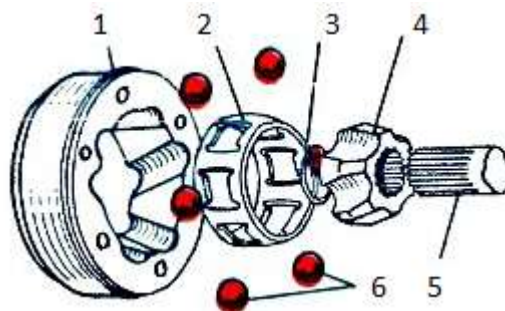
Кульковий шарнір з непаралельними діючими канавками типу «Рцеппа-Лебро» [6]: 1 – корпус; 2 – сепаратор; 3 – запірне кільце;
